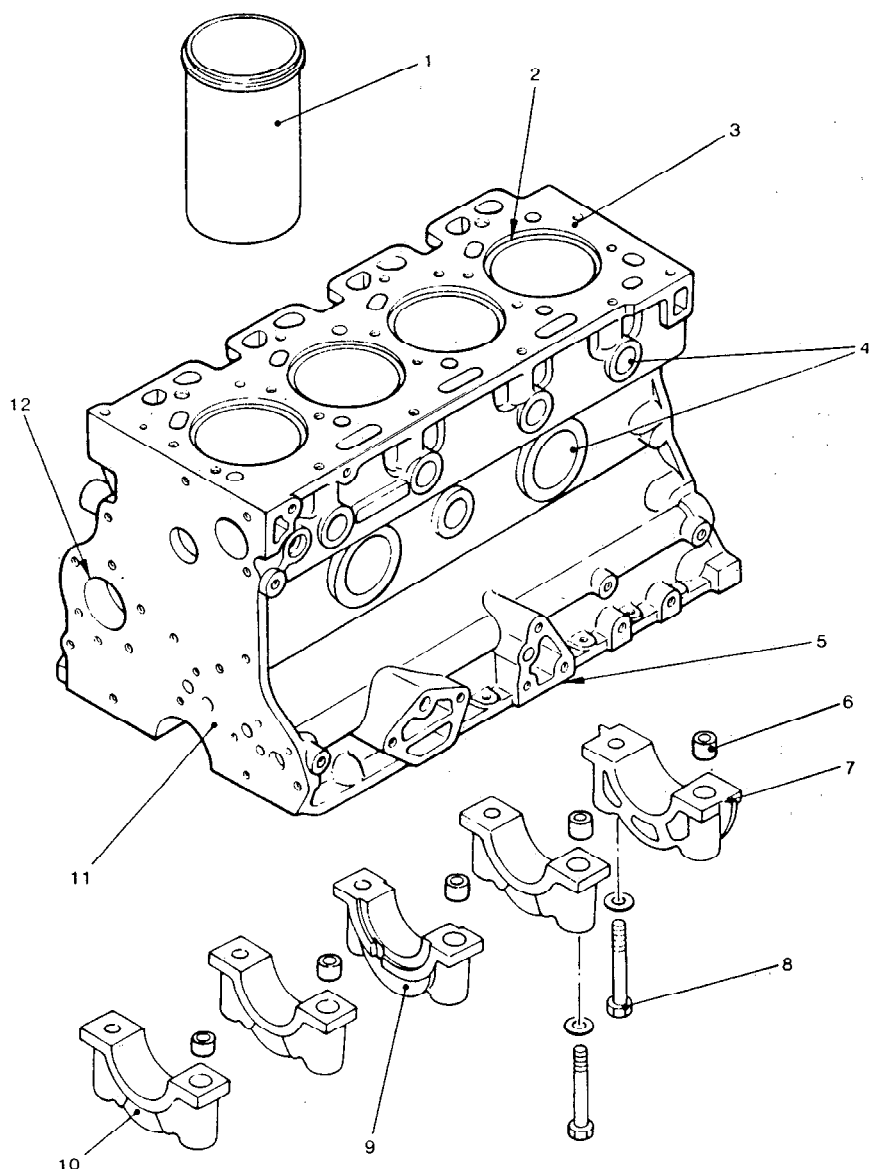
Bloque de cilindros de un motor de cuatro cilindros: 1 camisa de cilindro, 2 rebajo, 3 bloque, 4 tapones de expansión, 5 cara de montaje, 6 pasador tubular, 7 cojinete principal trasero, 8 tornillo de tapa de cojinete, 9 cojinete central con caras de empuje, 10 cojinete principal delantero, 11 cavidad para cojinete principal, 12 cavidad para el árbol de levas
